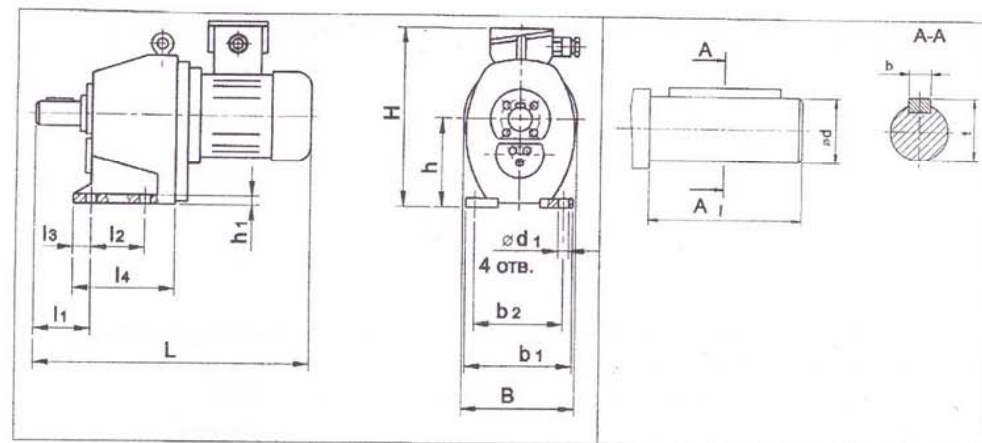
Габаритные и присоединительные размеры . Исполнение на лапах. Исполнение вала
